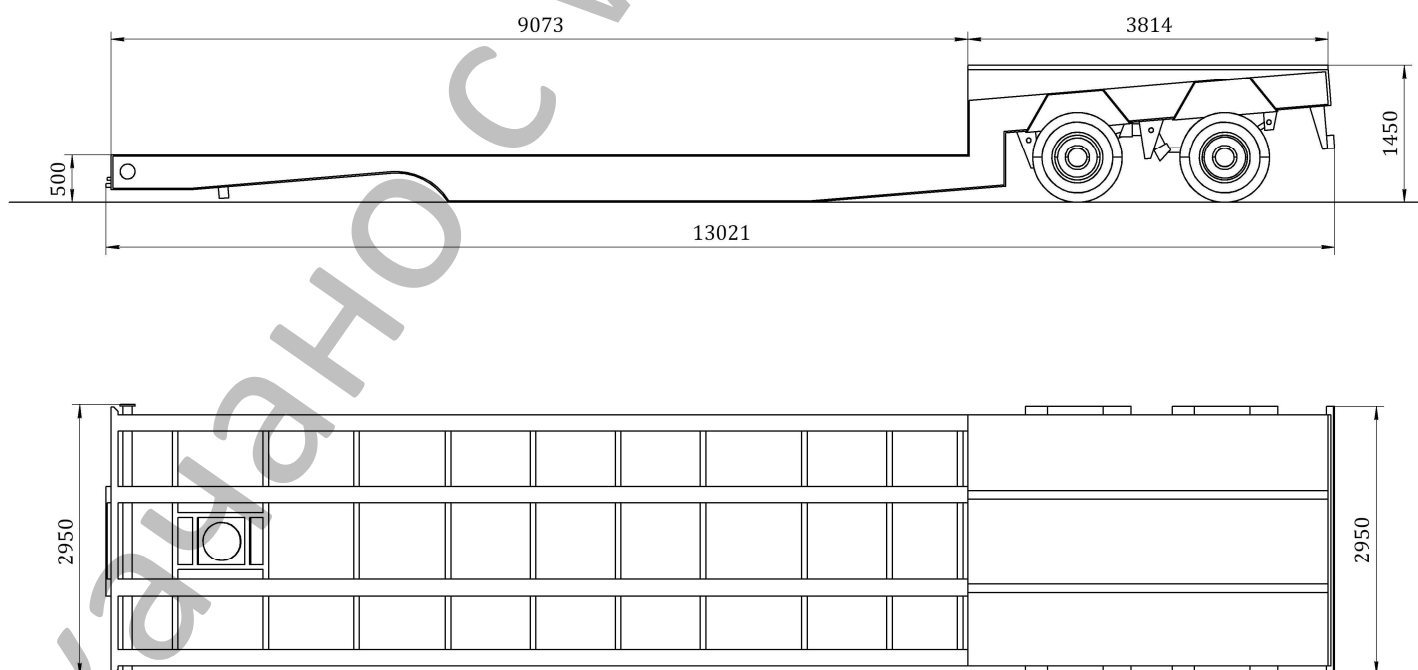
Общий вид полуприцепа 9420-0000010
